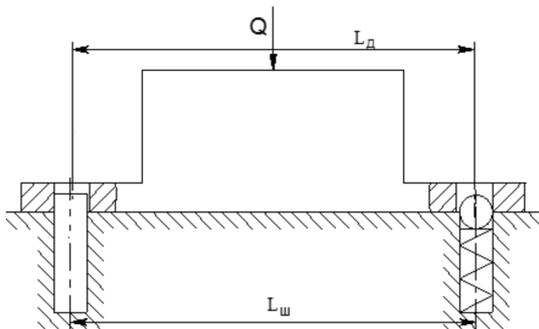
Установка заготовки на один цилиндрический палец и сферическую поверхность
